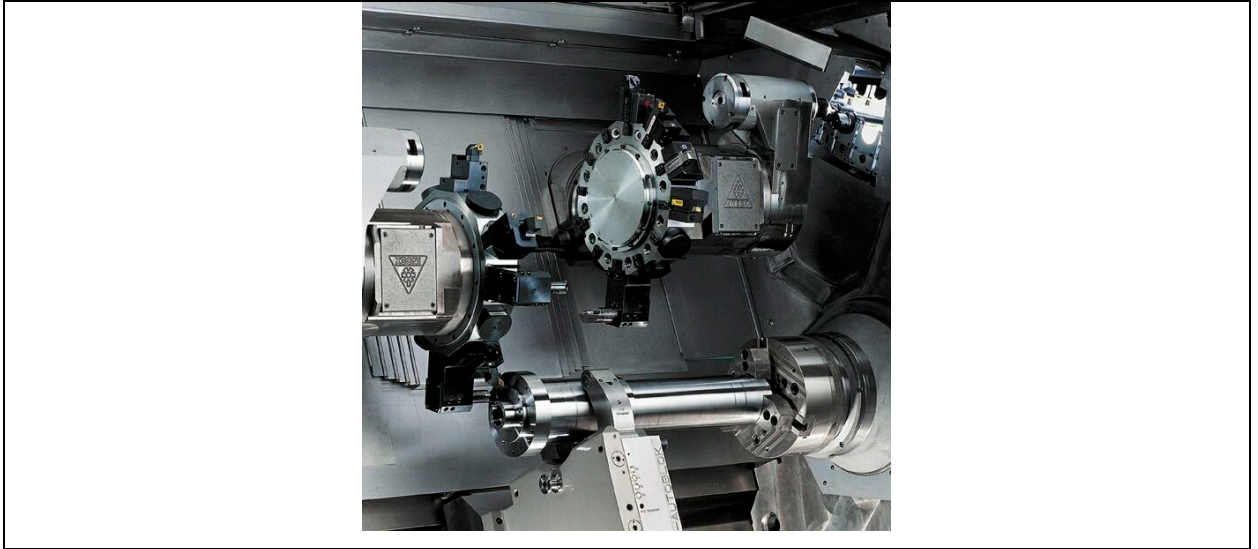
Самоцентрувальний люнет в конструкції верстату з ЧПУ
